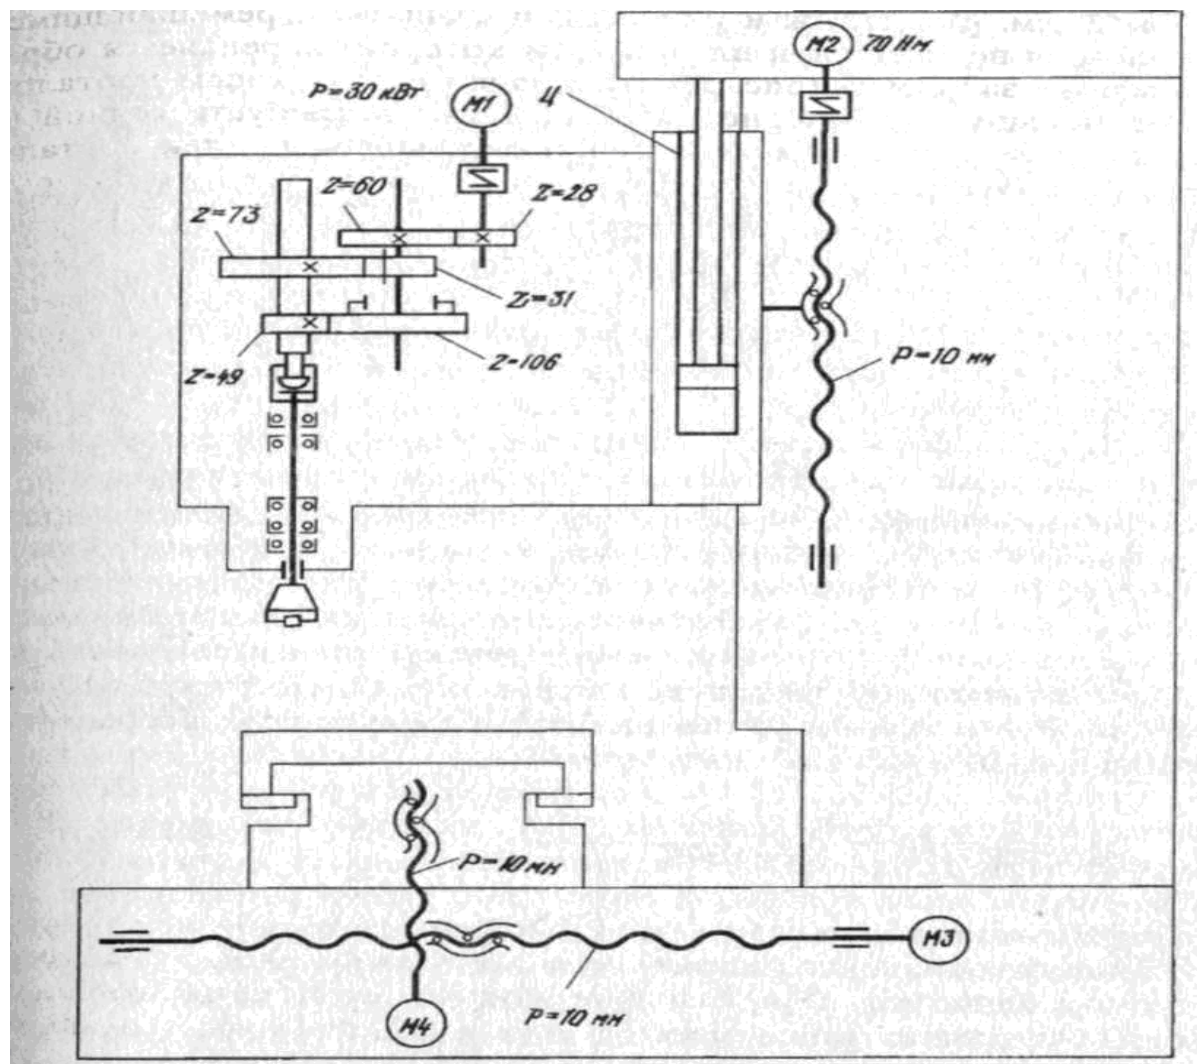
Кинематическая схема станка с ЧПУ.
